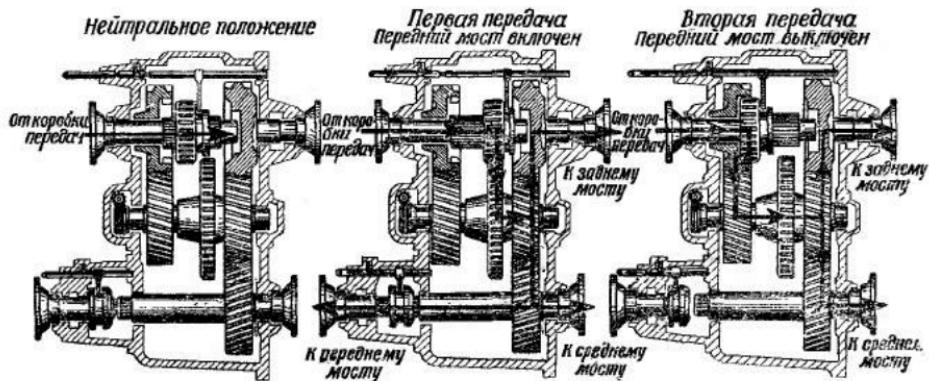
Схема зацепления шестерен раздаточной коробки на различных передачах
